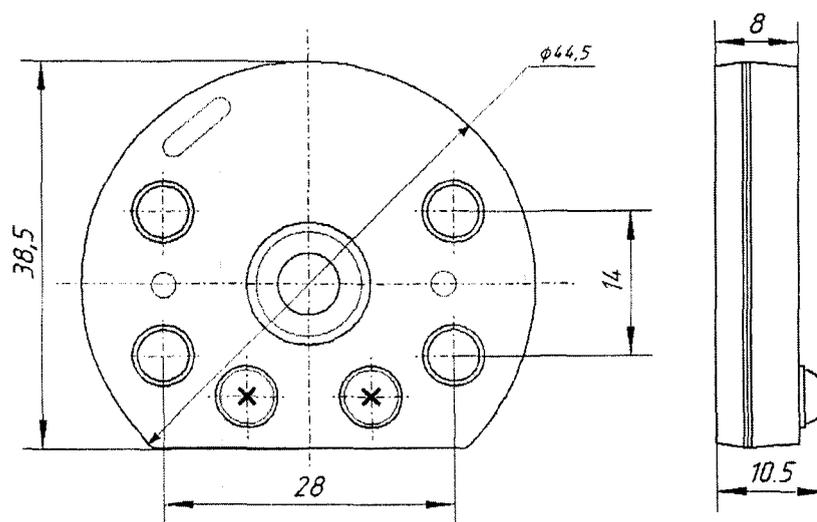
Преобразователь в корпусе Т для установки внутри клеммной головы ПП
